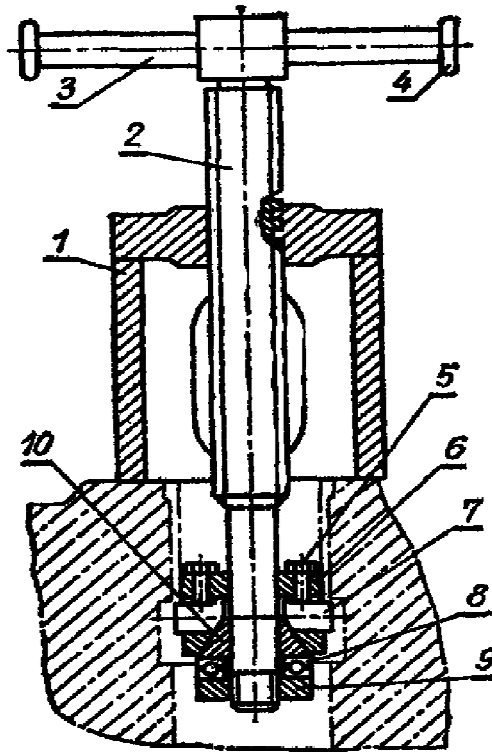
Пристосування для знімання втулок 1—упор; 2—силовий гвинт; 3—вороток; 4—опорне кільце; 5—гвинти; 6—корпус; 7—зажим; 8—упорний підшипник; 9—гайка; 10—корпус
